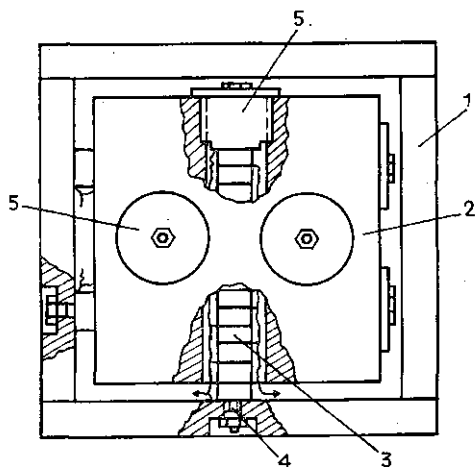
Общий вид приемника ускорений: 1 — корпус, 2 — груз, 3 — пьезоэлементы, 4 — стяжная шпилька, 5 — крышка
